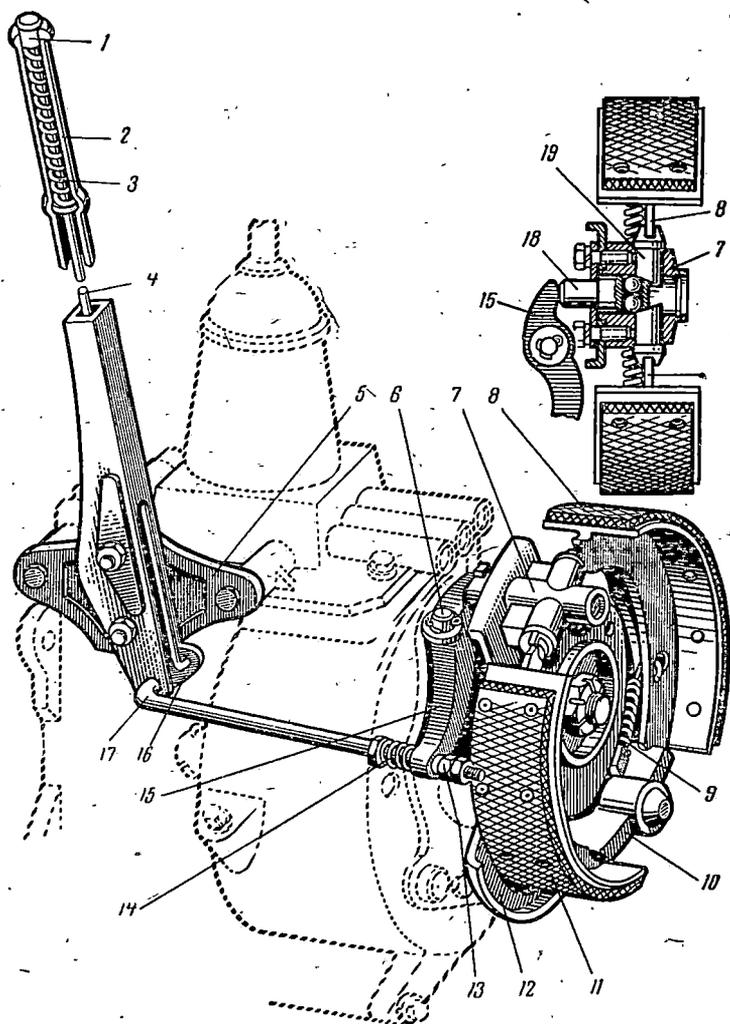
Ручной тормоз автомобиля ГАЗ-51А:
